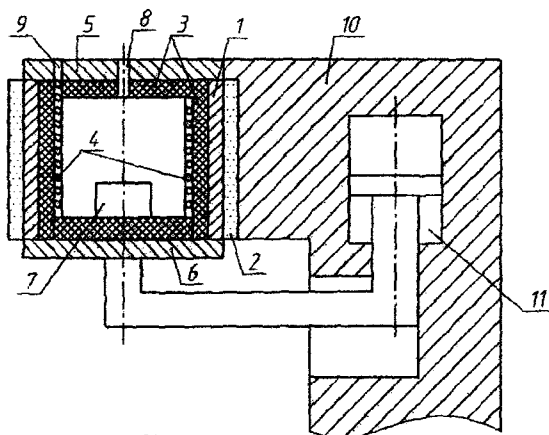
Рабочая зона гидростата с нижней загрузкой: 1 – корпус газостата; 2 – упрочняющая обмотка (лента металлическая (бандаж)); 3 – теплоизоляция; 4 – нагревательные элементы; 5 – верхняя крышка; 6 – нижняя крышка; 7 – обрабатываемая заготовка; 8 – отверстие для подвода газа; 9 – отверстие для подвода электрических проводов; 10 – станина; 11 – гидроцилиндр для опускания и поднятия нижней крышки 6
